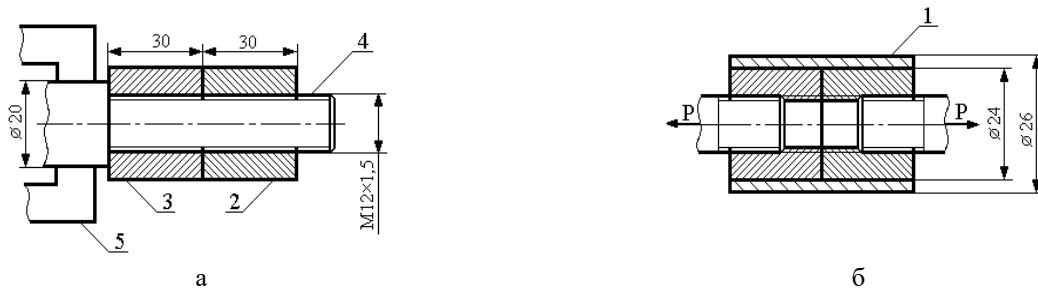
Схема визначення когезійної міцності покриттів: а – схема підготовки зразка; б – схема випробування; 1 – шар покриття; 2, 3 – втулки, що мають внутрішню різьбу; 4 – центральний гвинт; 5 – патрон обертача
